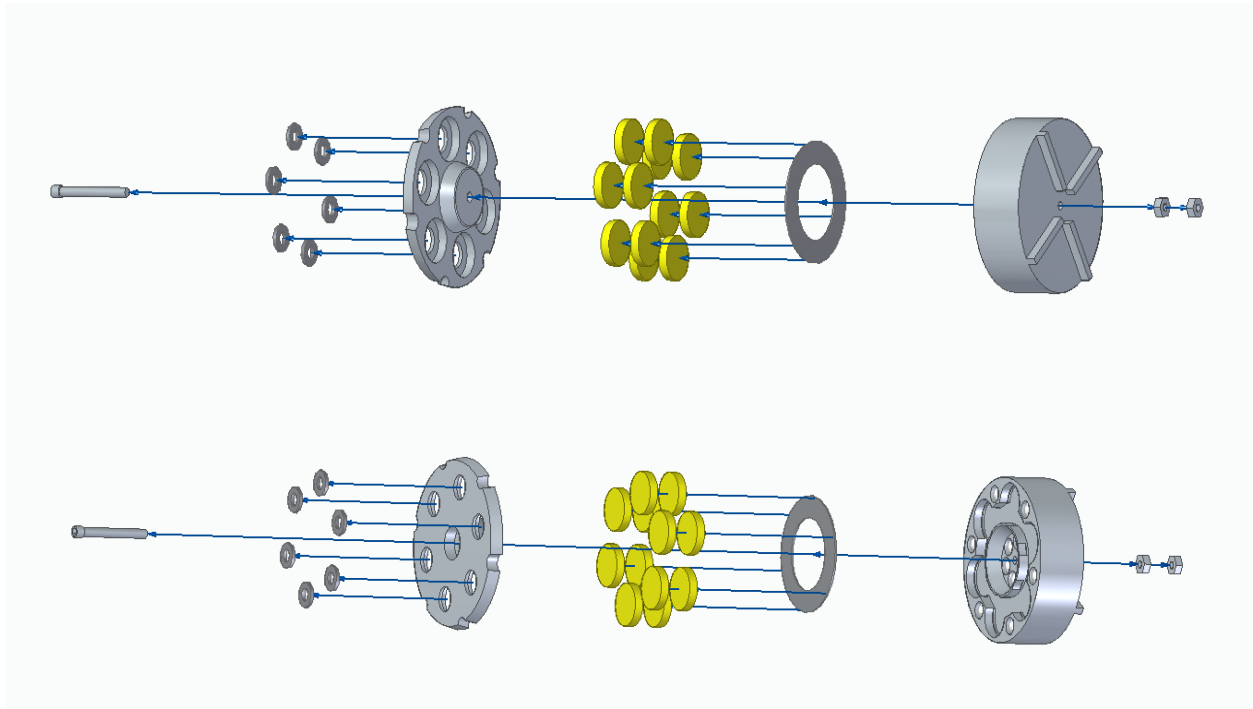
15. Vistas explosionadas del quinto diseño.
